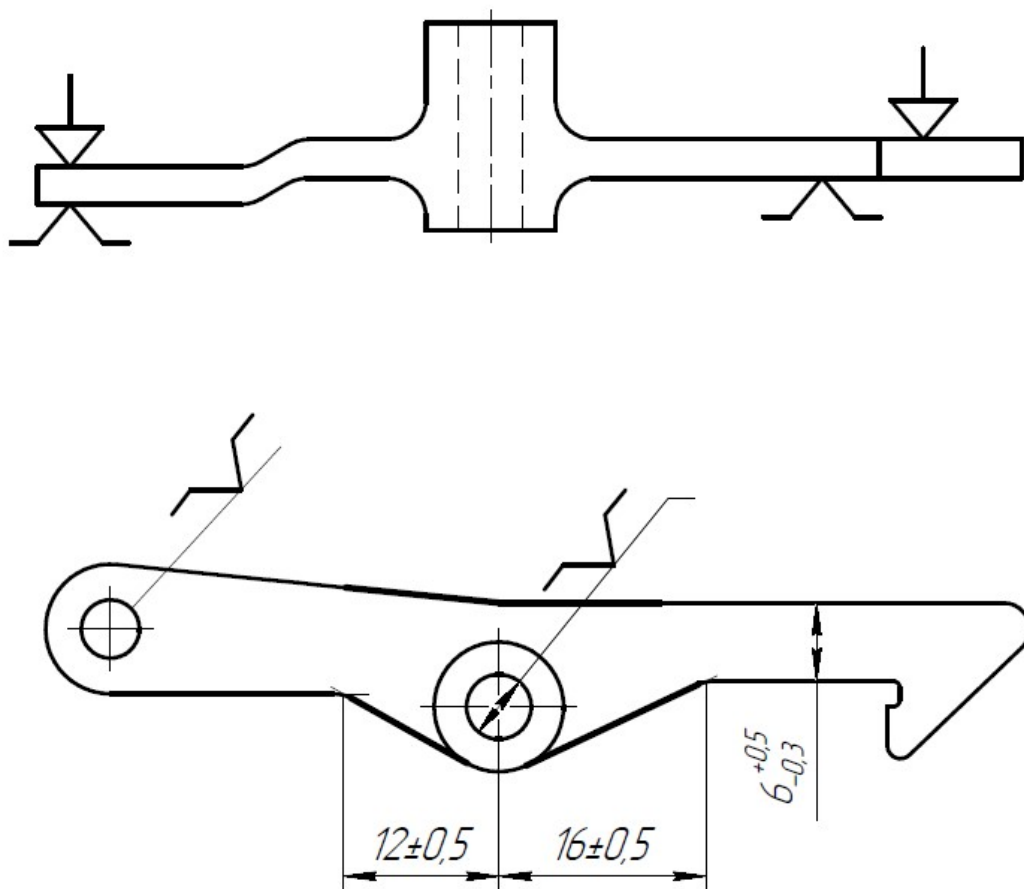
Схема базування деталі при фрезерній операції 055
